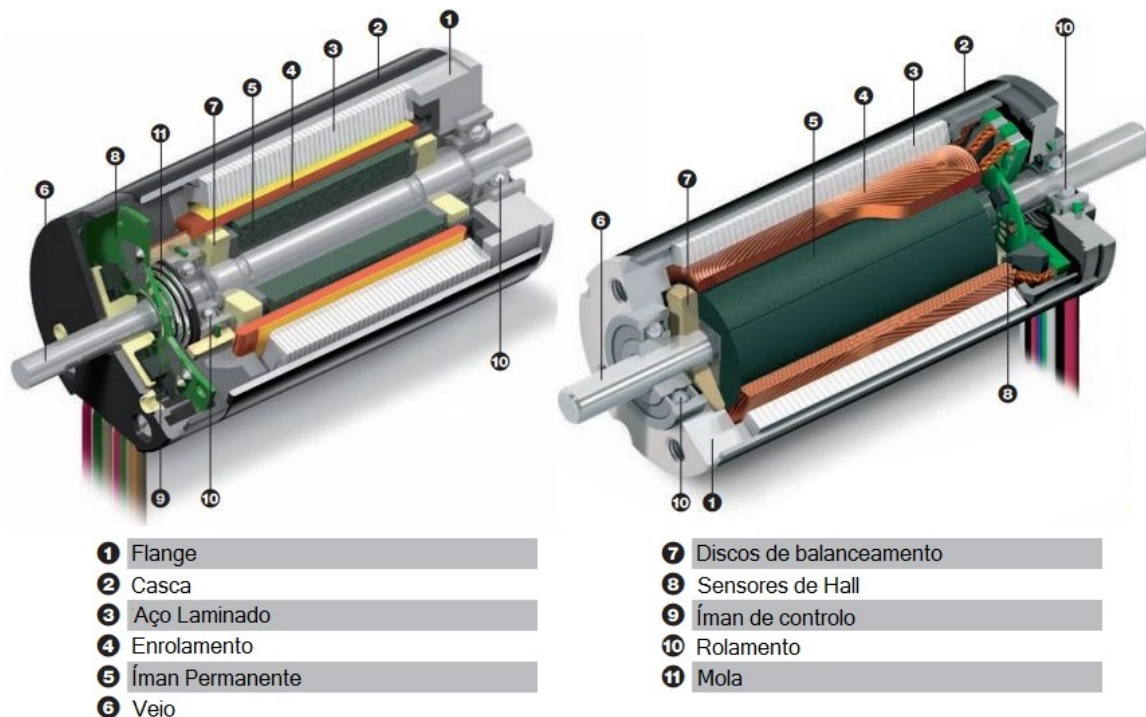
Anatomia de um motor BLDC com rotor interno (Adaptado [10]).
